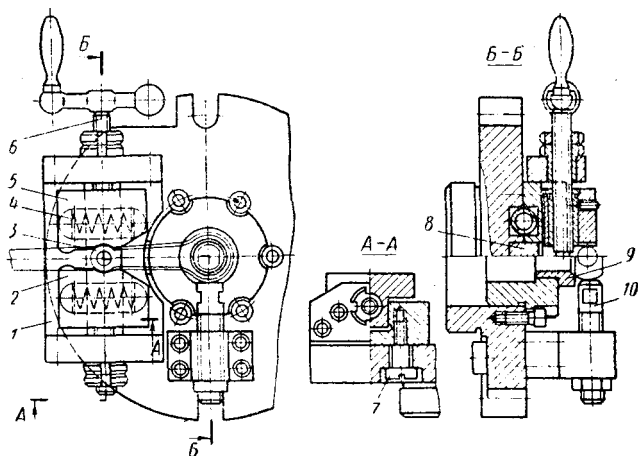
Приспособление к горизонтально-протяжному станку для крепления рычагов
